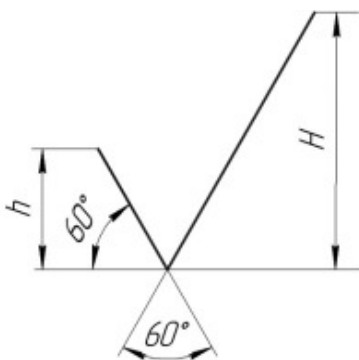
Обозначение шероховатости поверхности без указания способа обработки
